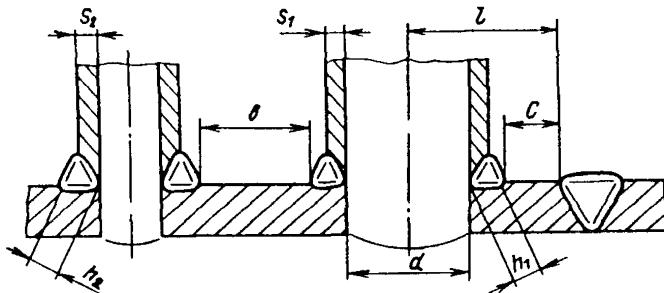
Расположение сварных швов приварки патрубков.
